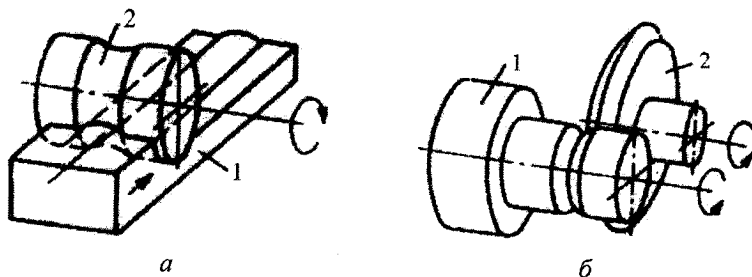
Обробка фасонних поверхнь: *а* – фрезерування профільним інструментом; *б* – кругове профільне фрезерування (*1* – заготовка; *2* – інструмент)
